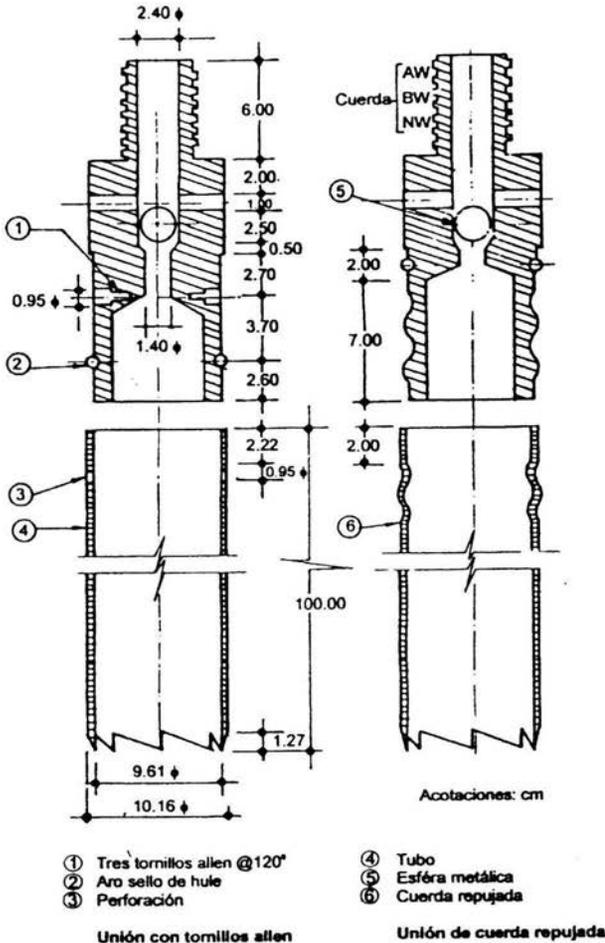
Muestreador de tubo dentado con válvula esférica de pie
